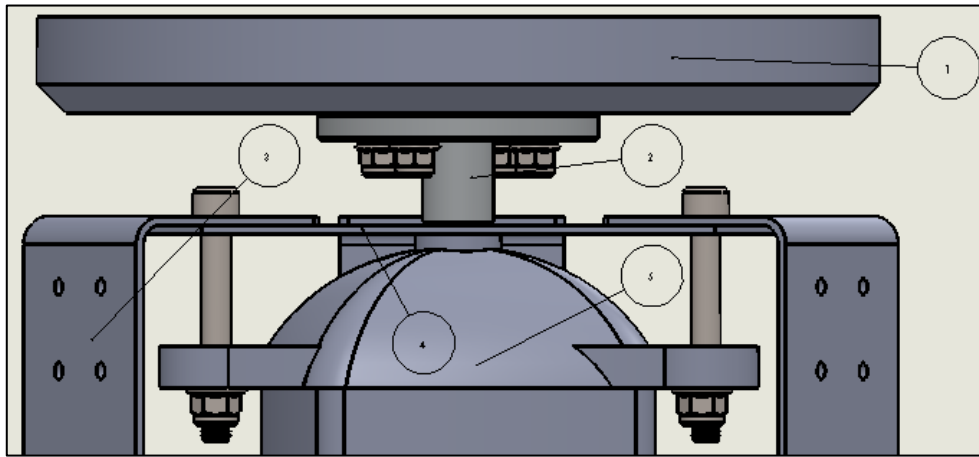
Transmission du mouvement du moteur vers le disque rotatif
